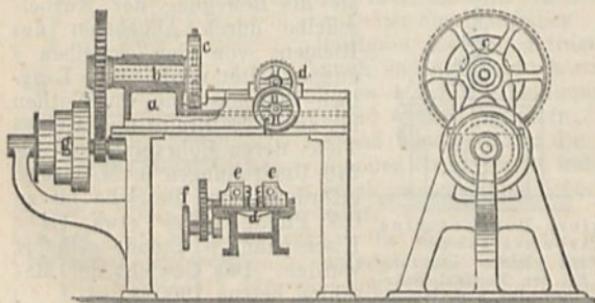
, 122, 123. Sellers'sche Schraubenschneid-Maschine.
